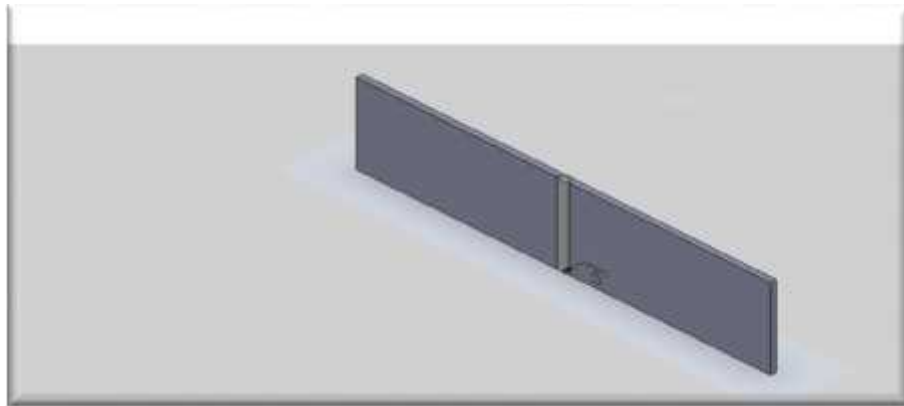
Assemblage des deux pièces avec cordon de soudure de forme V.
